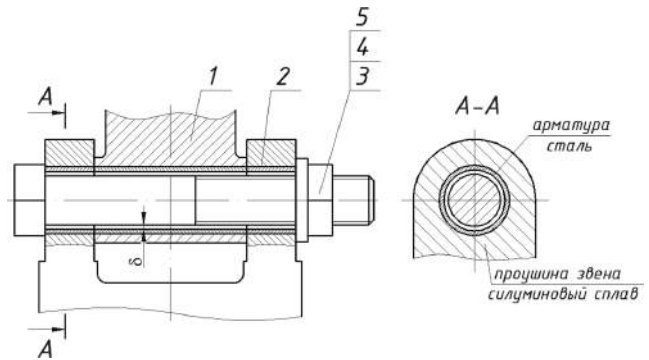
Болтовое соединение шлиц-шарнира стойки шасси:
